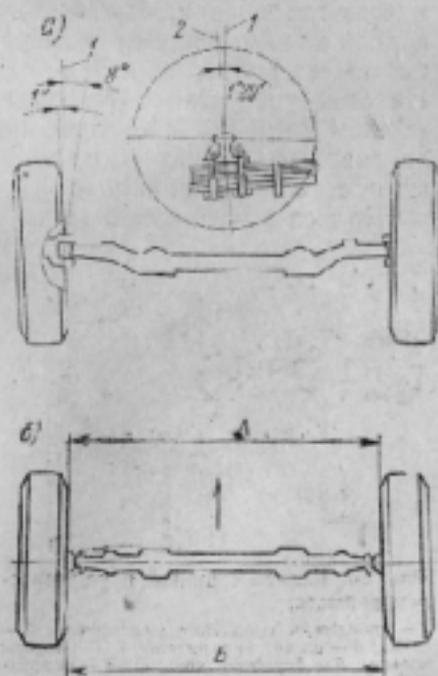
Развал колес; поперечный наклон шкворня и сходжение колес: 1 — вертикаль; 2 — ось шкворня
